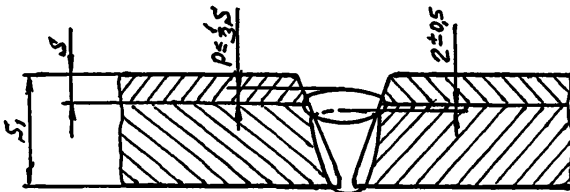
Усиление переходного слоя шва двухслойной стали
